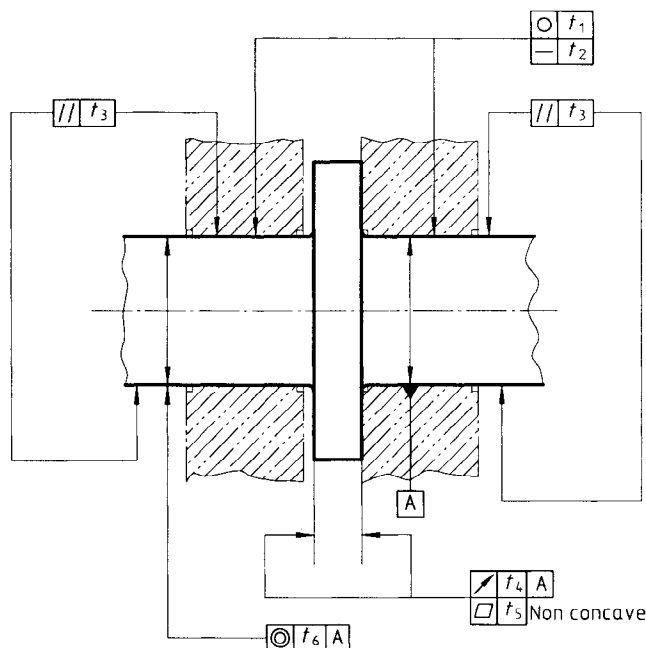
Arbre à collet de butée à collerette pour palier radial, capable de supporter une charge des deux côtés — C
